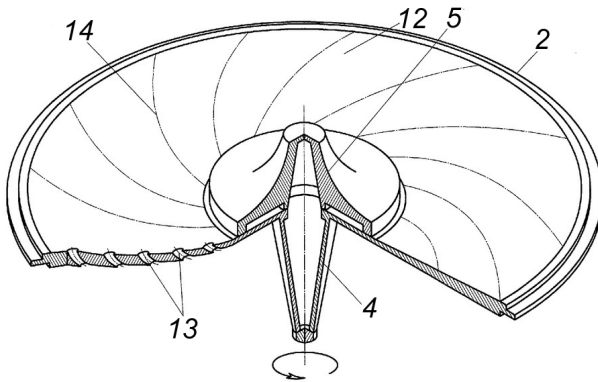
Схема апарата для готування цукрової вати з механізмом видачі паличок
